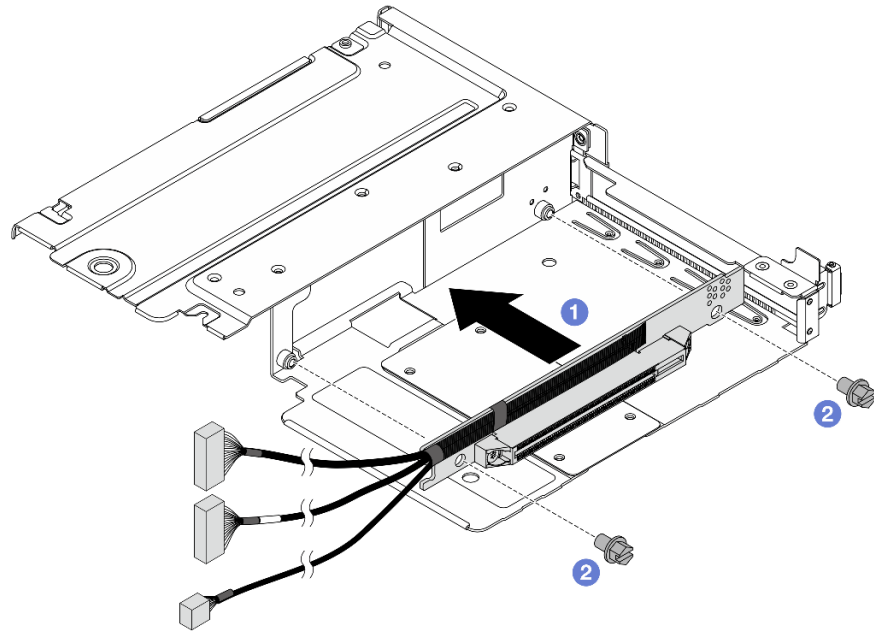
Installation de la carte mezzanine dans un boîtier pleine hauteur
